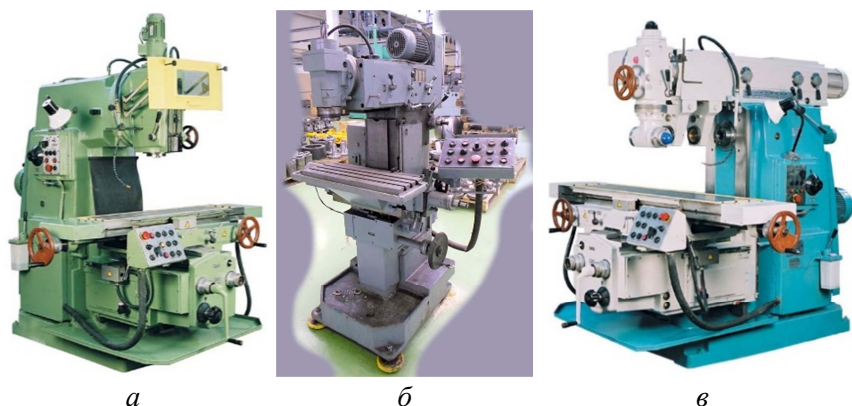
Фрезерные станки для обработки державок сборных резцов:
